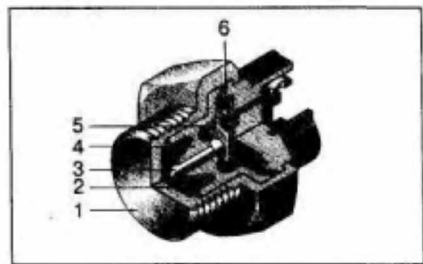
Датчик ТМ108 включения вентилятора: 1 — корпус; 2 — термобиметаллическая пластина; 3 — толкатель; 4 — направляющая толкателя; 5 — подвижный контакт; 6 — неподвижный контакт
